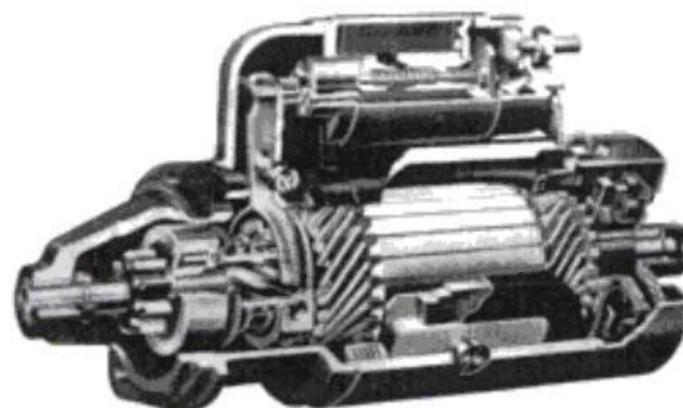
Motor de arranque seccionado para que pueda verse su interior y las principales piezas que lo componen.
